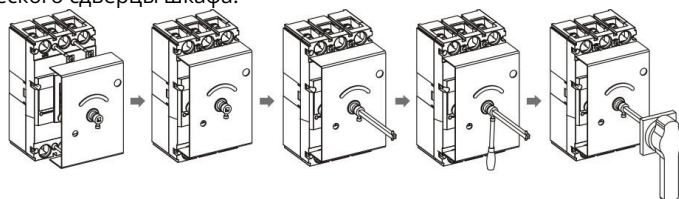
Схема установки рукояти на дверь шкафа РП-330
